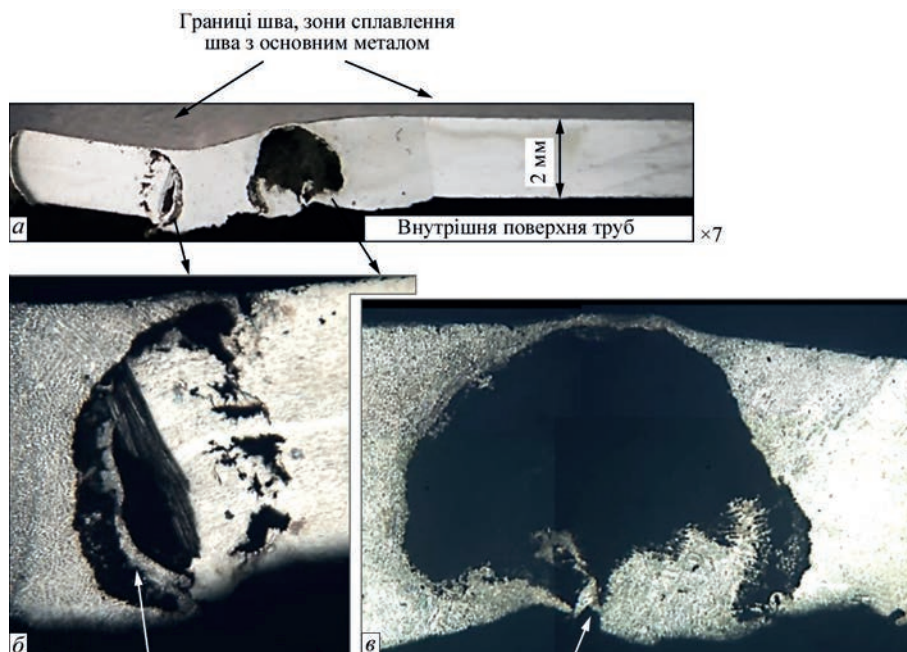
Наскрізні дефекти у шві: *а* – поперечний переріз зразка, $\times 7$; *б* – несплавлення шва з основним металом, корозія, $\times 27$; *в* – непровар кореня шва, корозія металу шва у порожнині з боку внутрішньої поверхні, $\times 27$
